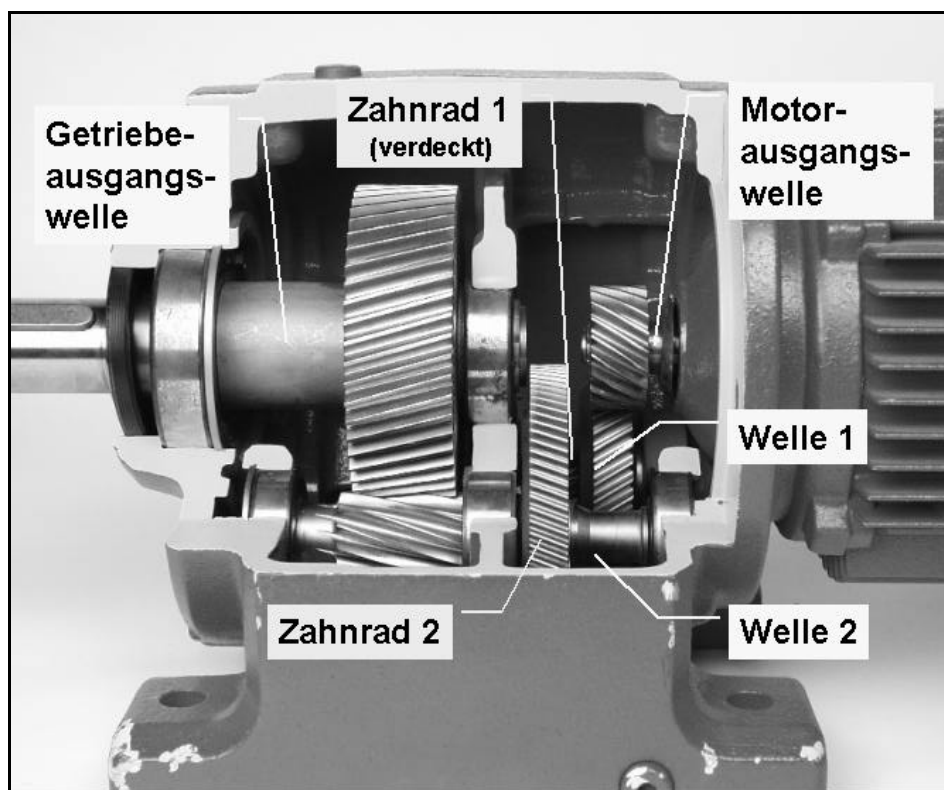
„Getriebemotor mit 3-stufigem schrägverzahnten mechanischem Getriebe“
